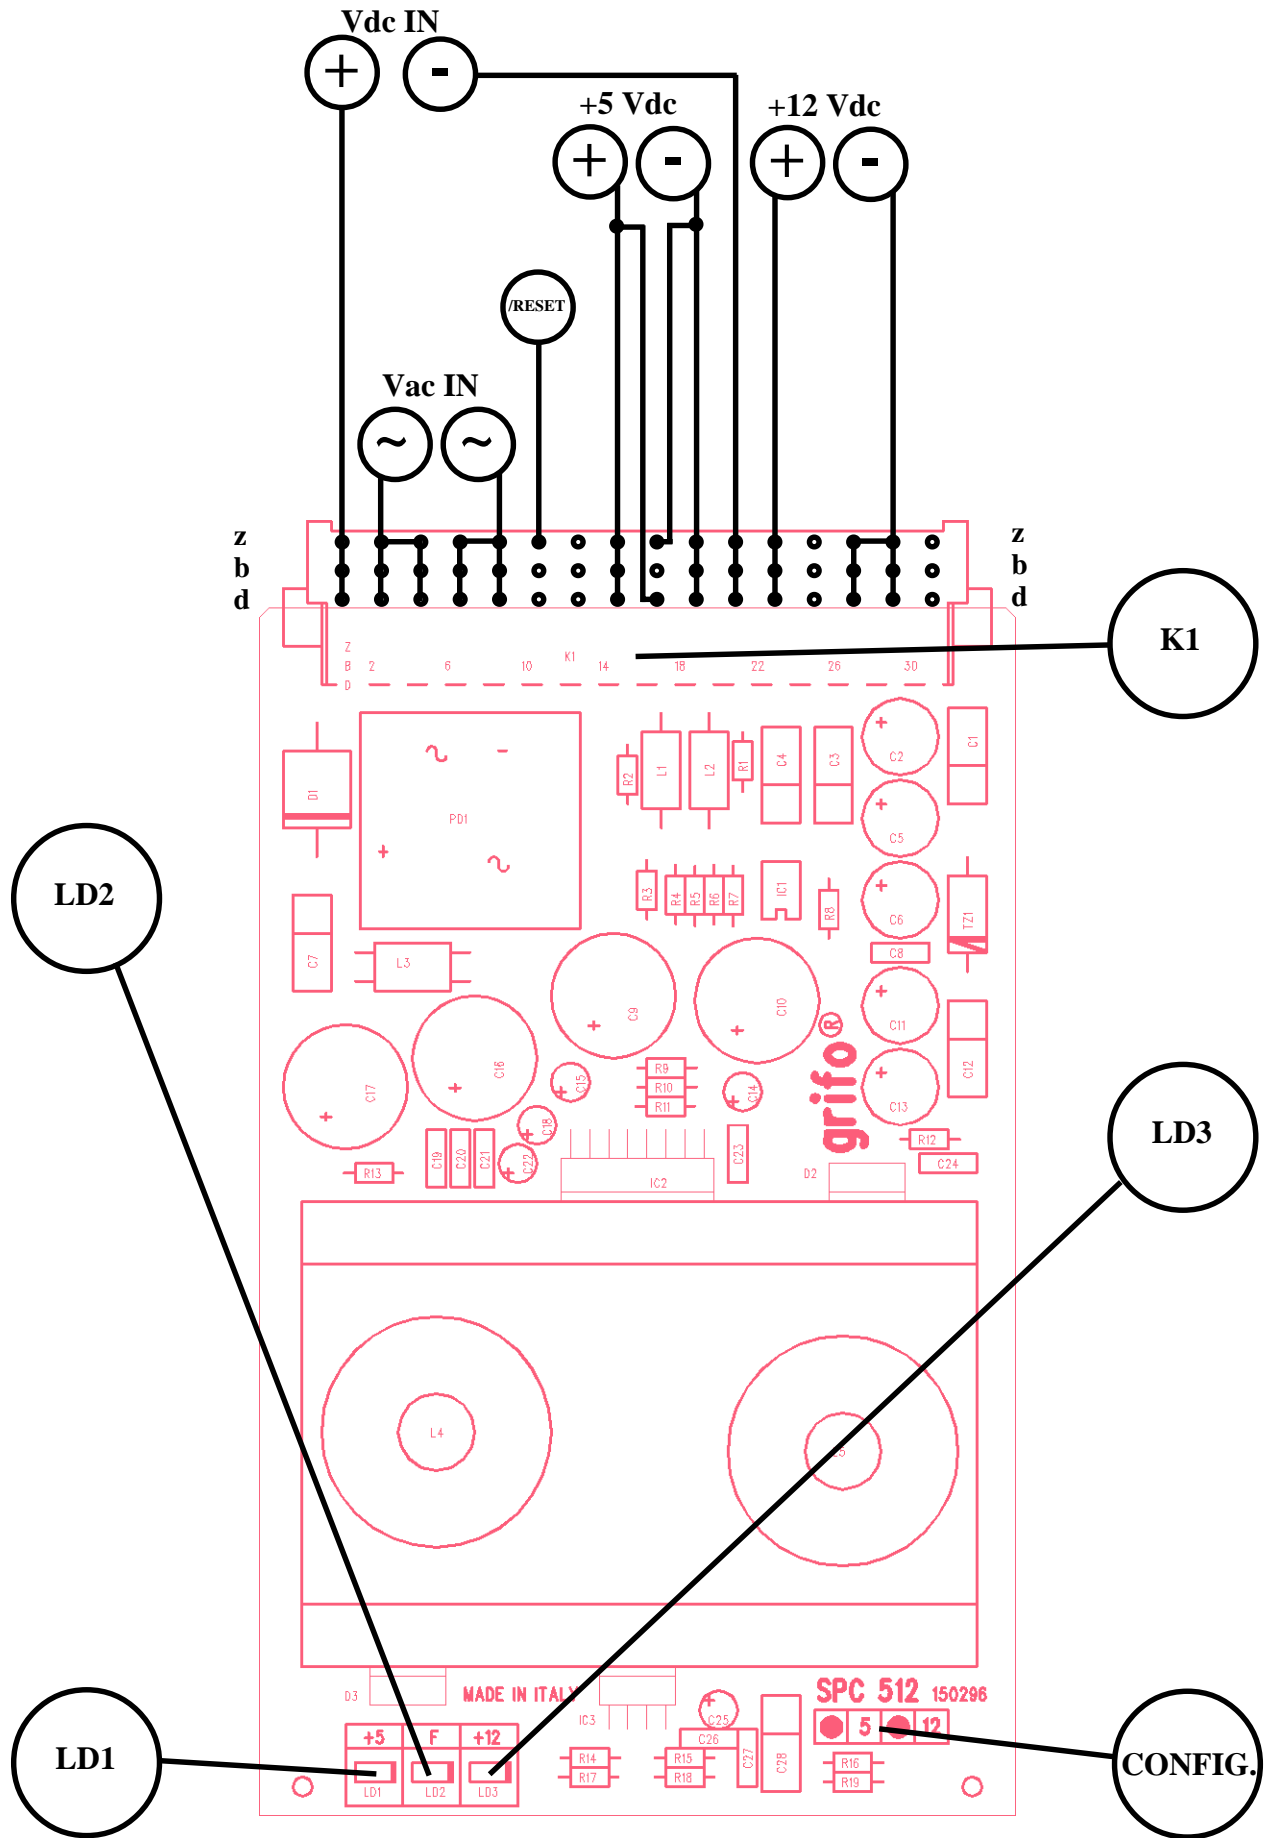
DISPOSIZIONE LED, CONNETTORI, COLLEGAMENTO COMPENSAZIONE ESTERNA
